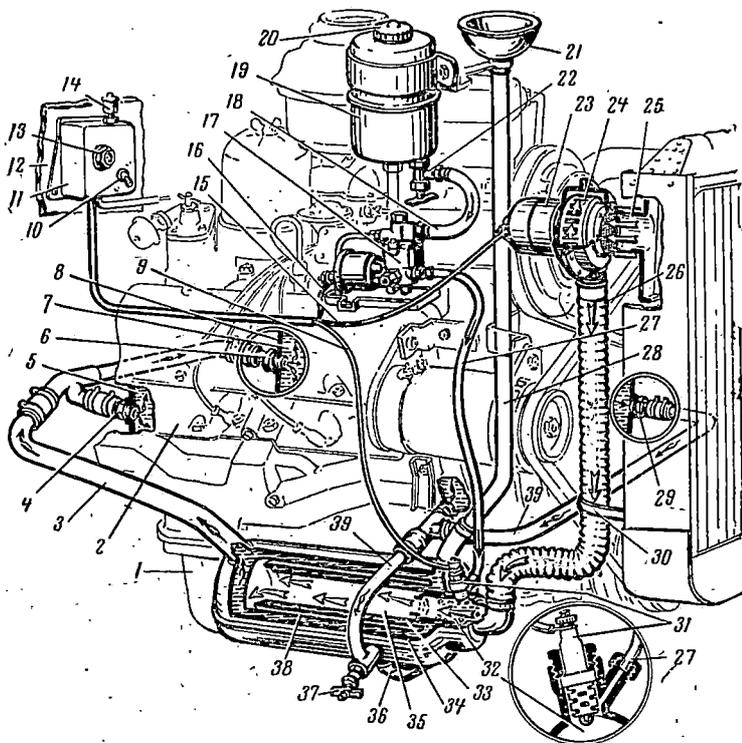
Пусковой подогреватель двигателя ЗИЛ-130:
